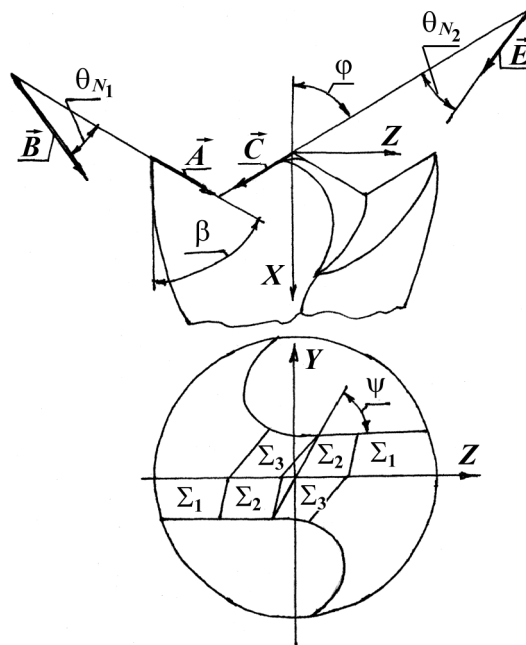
Схема определения геометрических параметров режущей части сверла с подрезающими режущими кромками
